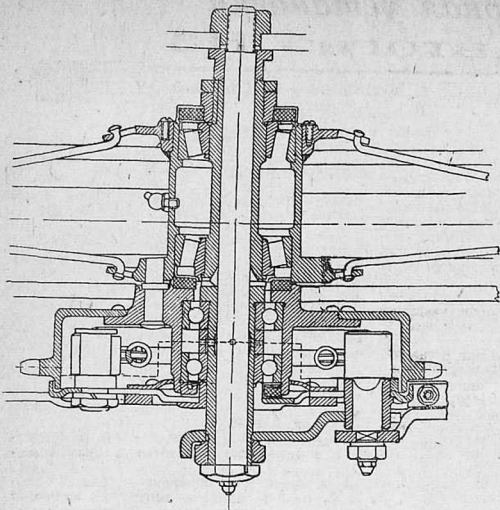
Задний колесный тормоз и ступица колеса АМ-600
